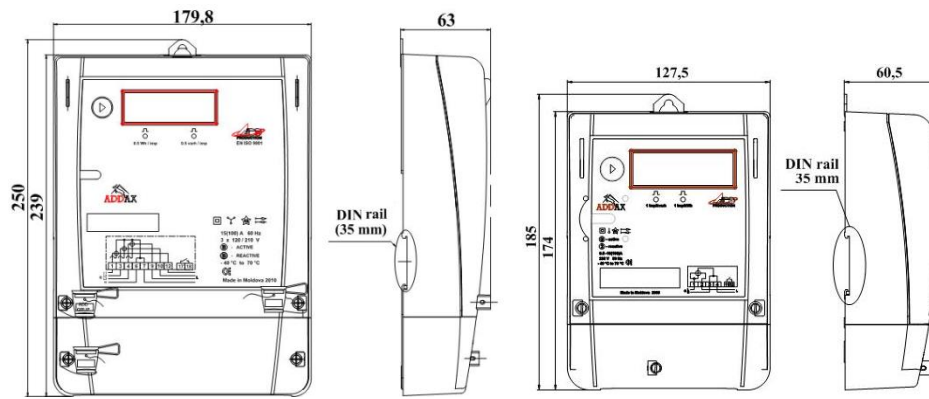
Общий вид и габаритные размеры счетчика с обычной крышкой клеммника
